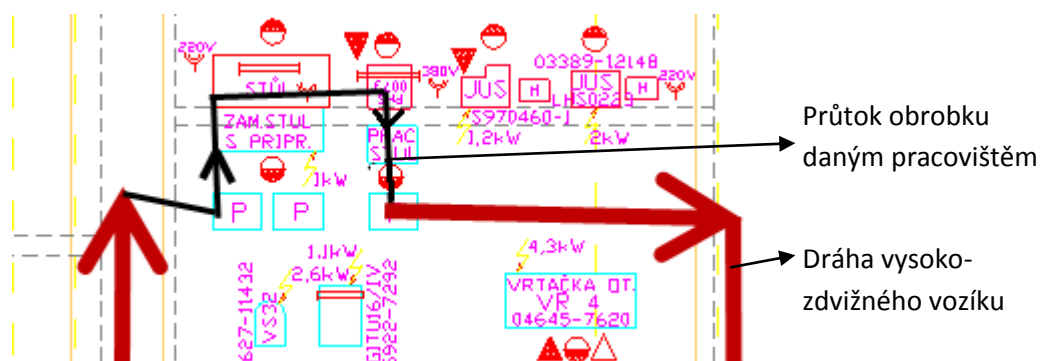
Průtok obrobku přes budoucí U-linku [28]
